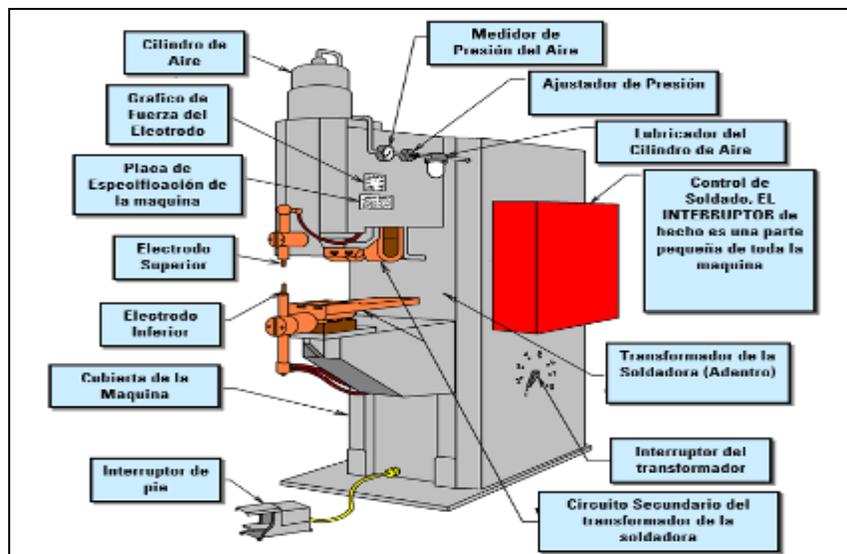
Descripción máquina de soldadura. Fuente: spot welding consultants
